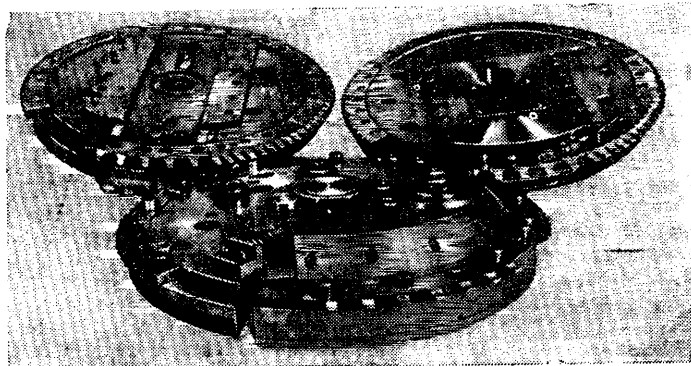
Круговые протяжки с подвижными элементами для нарезания цилиндрических зубчатых колес
